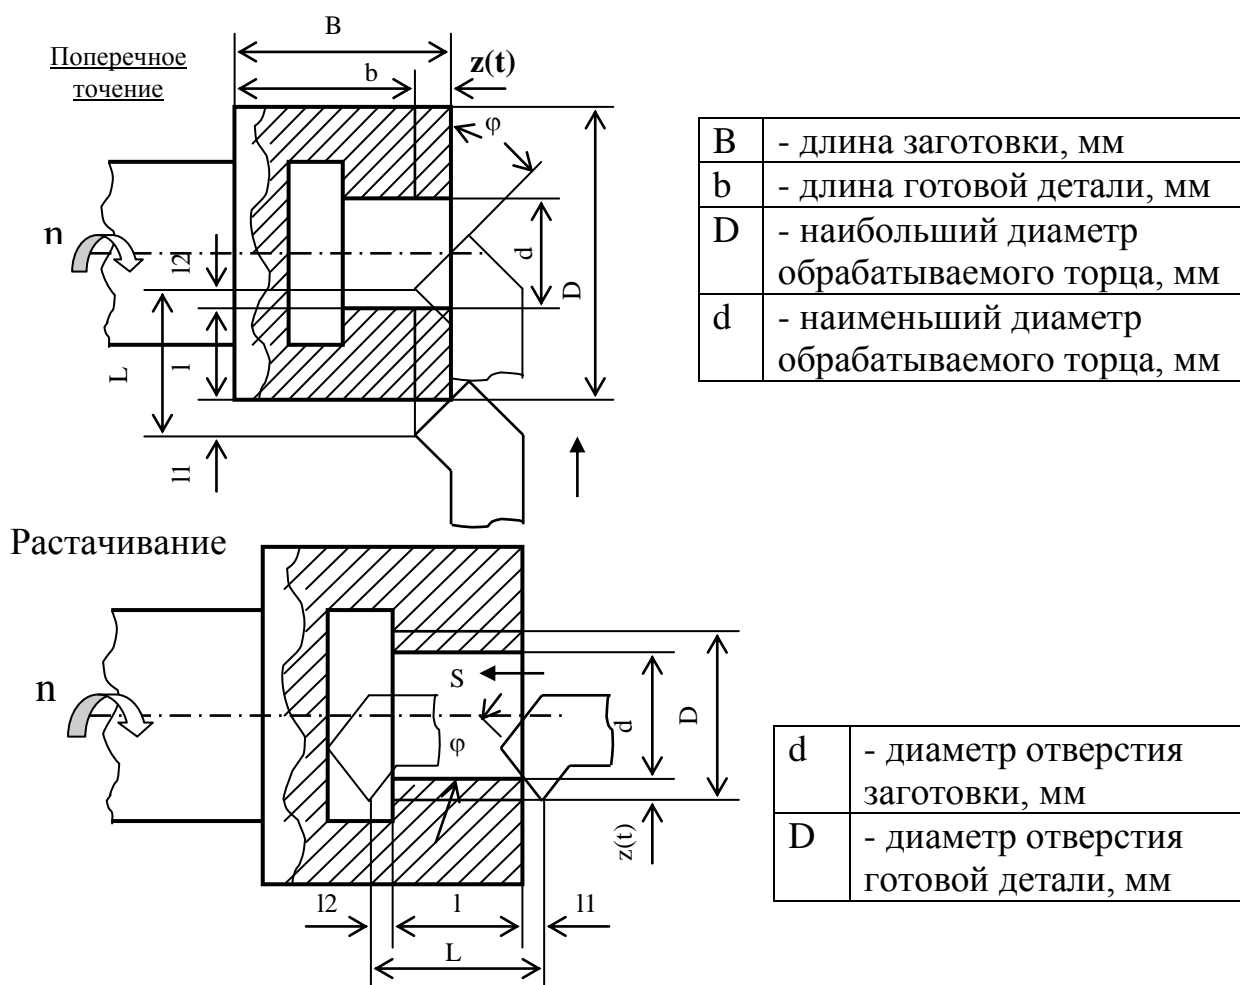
Схемы обработки наружных, торцевых и внутренних поверхностей
